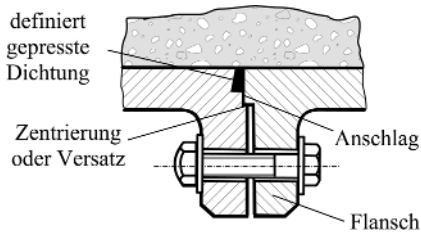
Flanschverbindung mit hygienegerechter Abdichtung.
